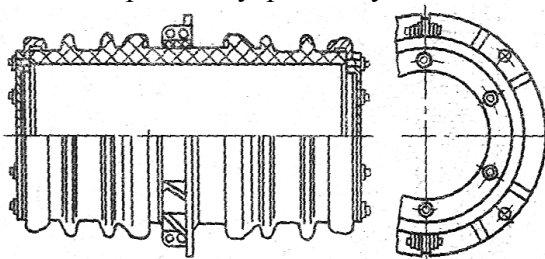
Проходной изолятор для внутренней установки 20 кВ, 8000 - 12 500 А
